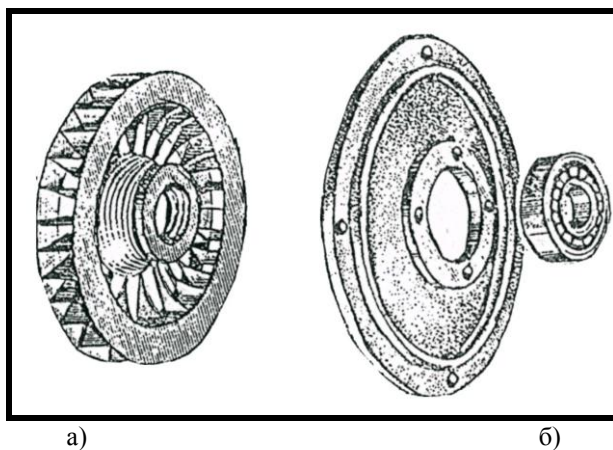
Общий вид вентилятора (а) и подшипникового щита (б)
